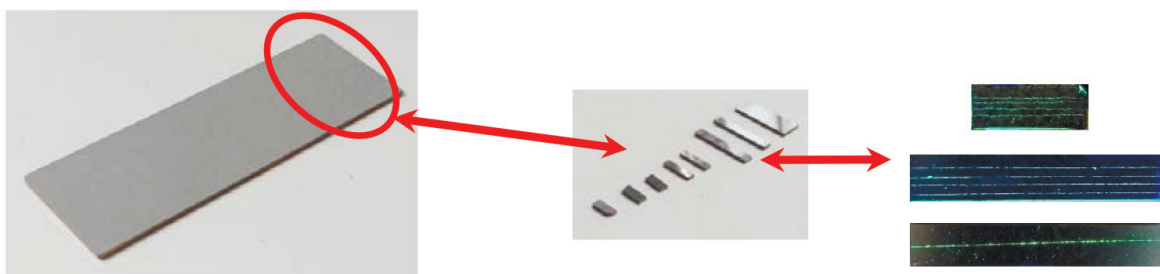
Вид изготовленных образцов для оценки качества нанесения и результаты их капиллярного экспертного контроля.
